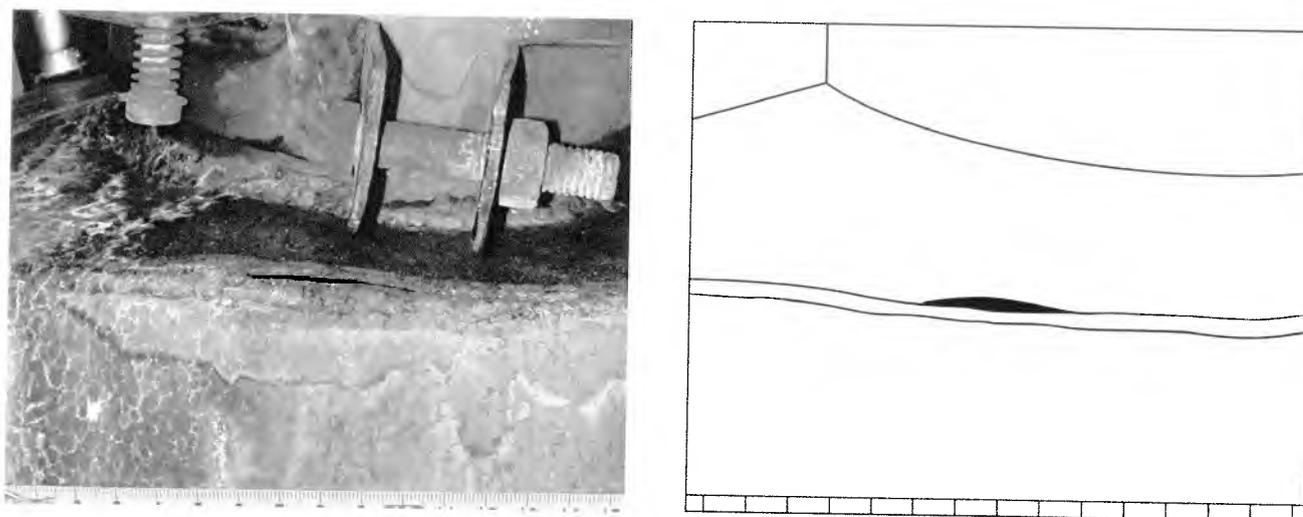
Сквозная продольная трещина углового сварного соединения обечайки сосуда с коническим днищем на фоне поверхности, окрашенной продуктами коррозии
